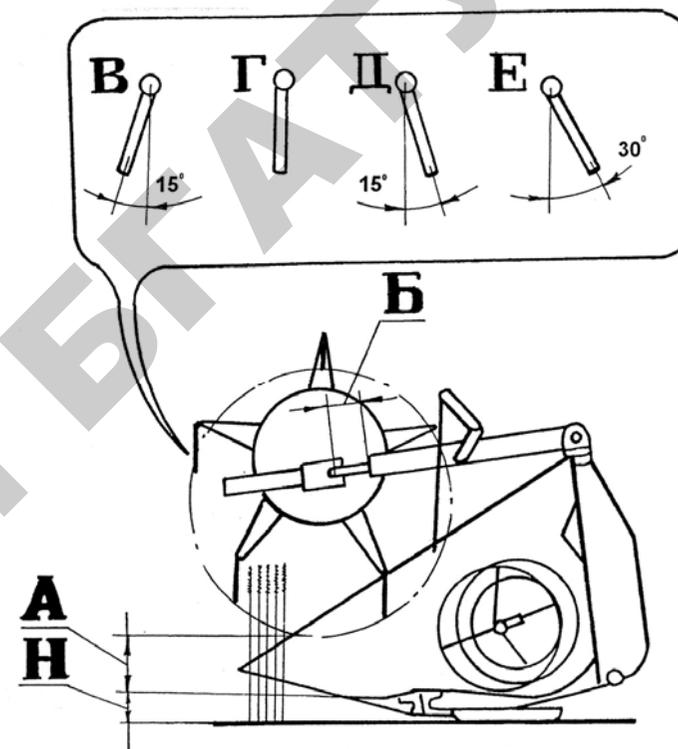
Схема установки мотовила при работе жатки: А — зазор между граблями и режущим аппаратом; Б — величина выступающей части штока гидроцилиндра перемещения мотовила по горизонтали; В, Г, Д, Е — положение граблей; Н — высота среза стеблей
